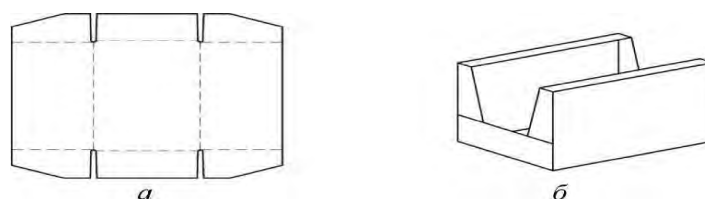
Развертка (а) и внешний вид (б) ящика лоткового типа
